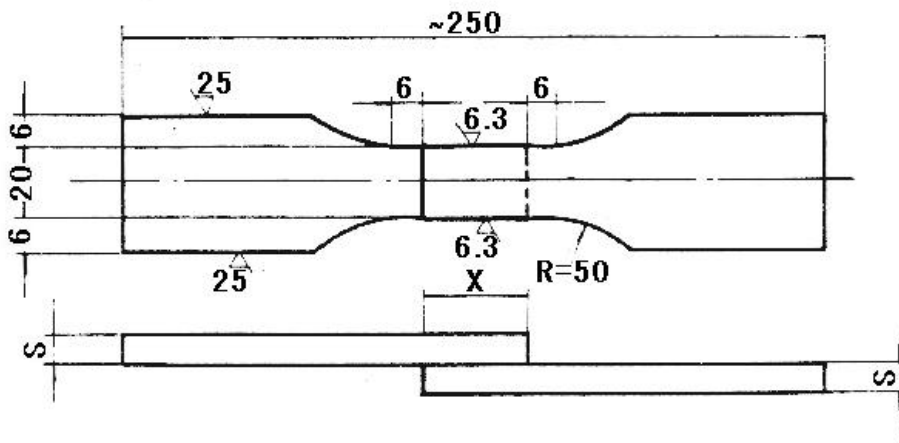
板状钎焊接头拉伸试样
